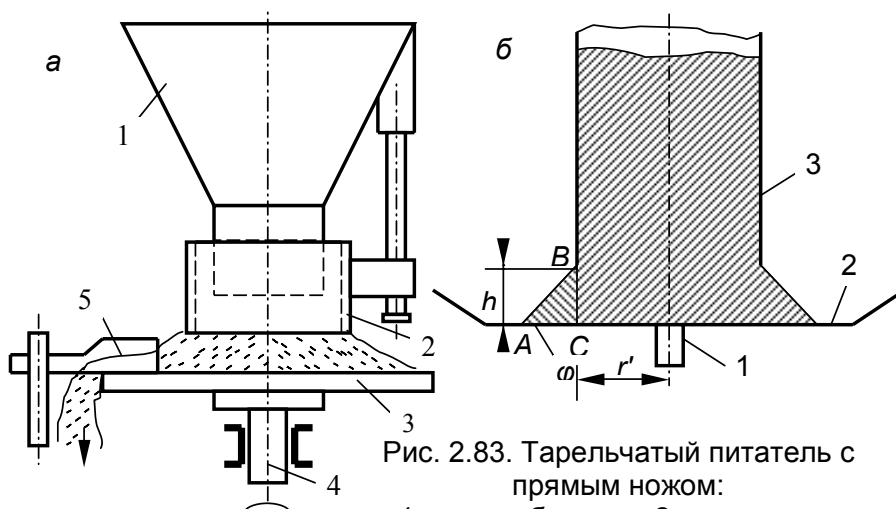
Тарельчатый питатель с прямым ножом:
